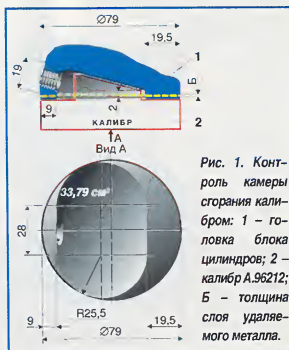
Контроль камеры сгорания калибром: 1 — головка блока цилиндров; 2 — калибр А.96212; Б — толщина слоя удаляемого металла.
